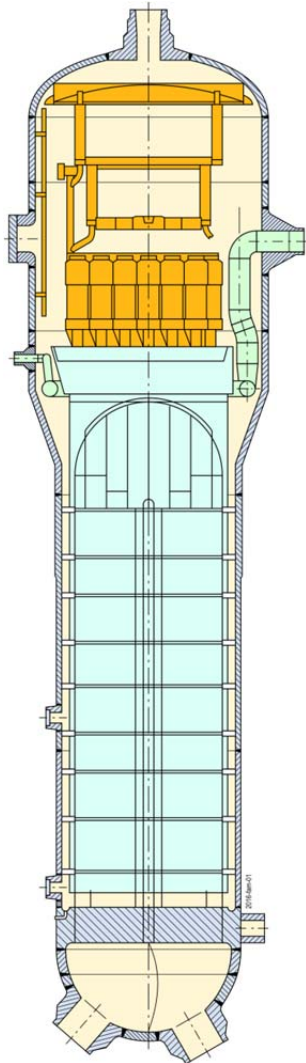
Schemazeichnung eines (Konvoi-) Dampferzeugers ohne Vorwärmkammer mit eingezeichneten Schweißnähten
